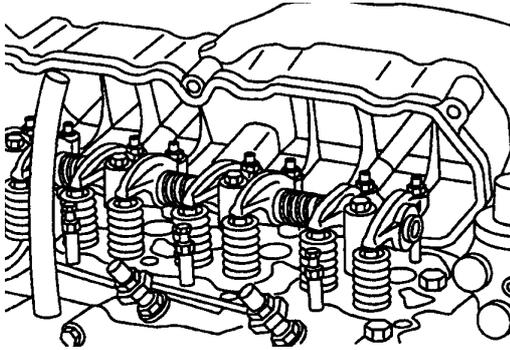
Abbau der Zylinderkopfhaube des MITSUBISHI-Motors
